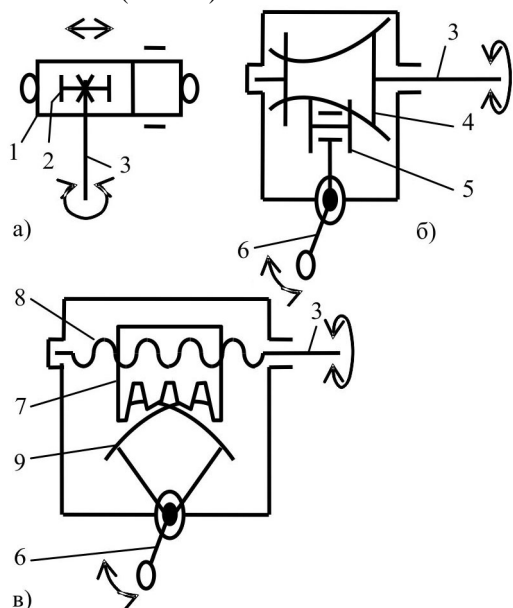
Схеми рейкової (а), черв'ячно-роликової (б) і гвинто-рейкової (в) кермових передач: 1 – рейка; 2 – шестерня; 3 – кермовий вал; 4 – черв'як; 5 – ролик; 6 – сошка; 7 – гайка-рейка; 8 – гвинт; 9 – зубчастий сектор
